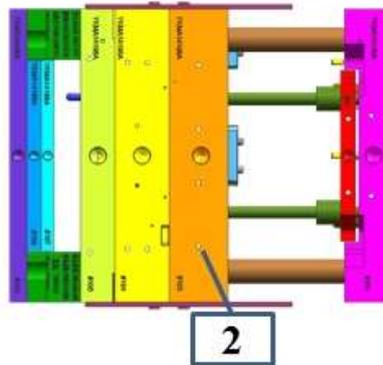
Desembalagem do Molde do Molde Dentro da Embalagem.
